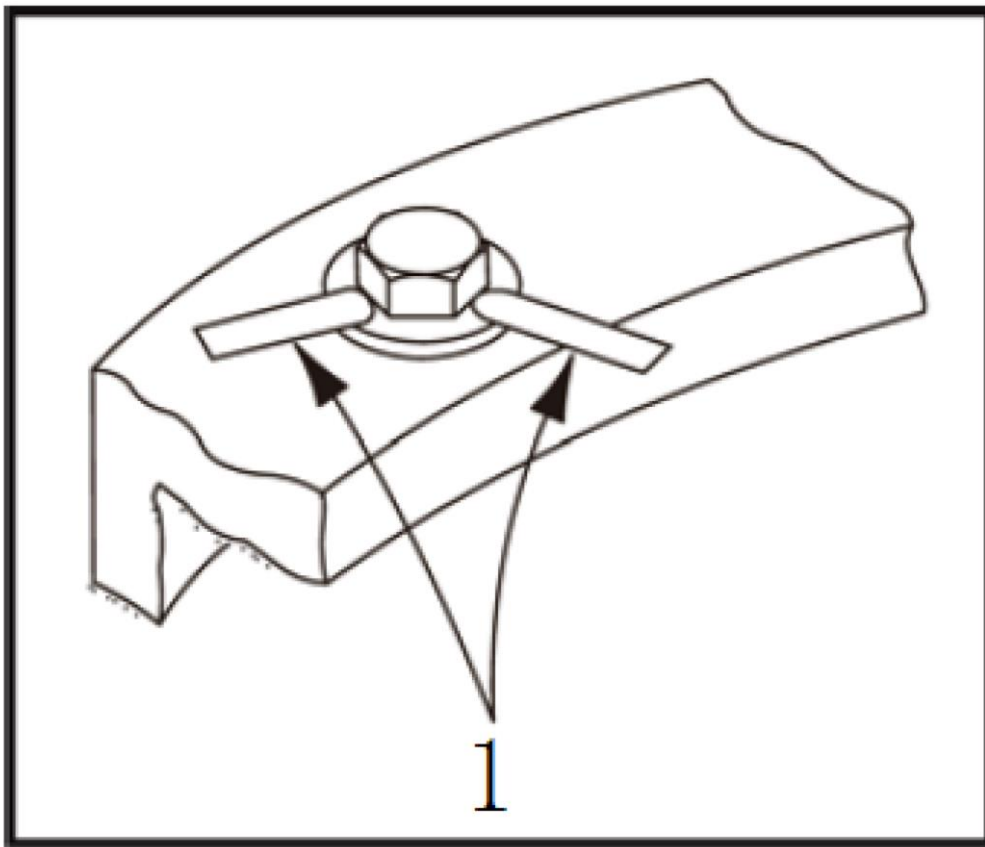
Inspeção do calibrador de folga do redutor rotativo
